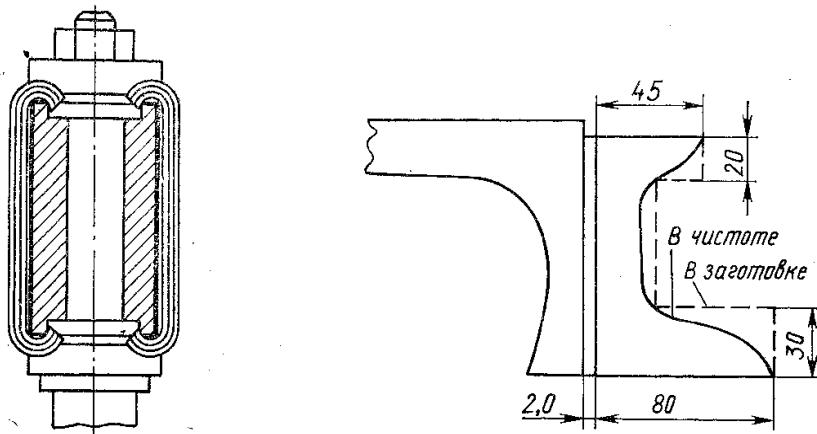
Шлифовальный валик для шлифования корпусов, грифов
